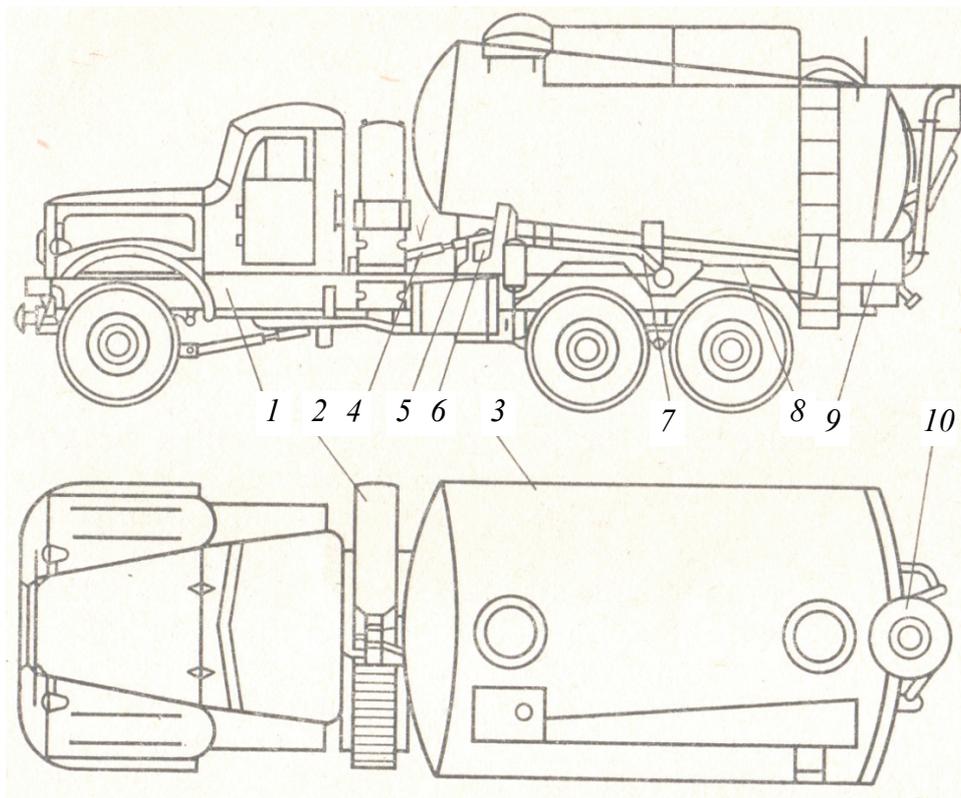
Агрегат смесительный ЗАС-30: 1 – кабина; 2 – коробка отбора мощности; 3 – цистерна; 4 – трансмиссия; 5 – ротационный компрессор; 6 – шестеренчатый насос; 7 – манифольд; 8 – система пневморазгрузки; 9 – пост управления; 10 – сепаратор
